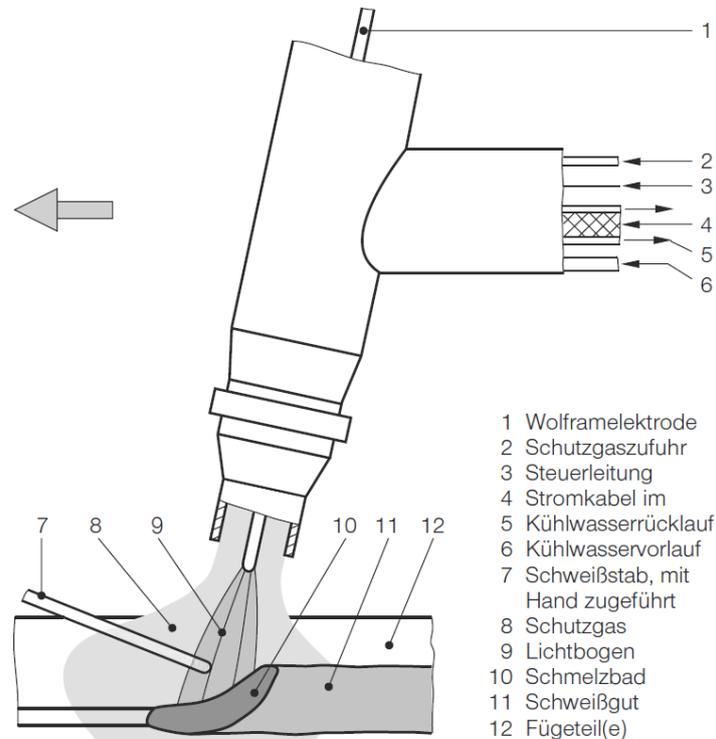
WIG-Schweißverfahren [17, p. 160]
